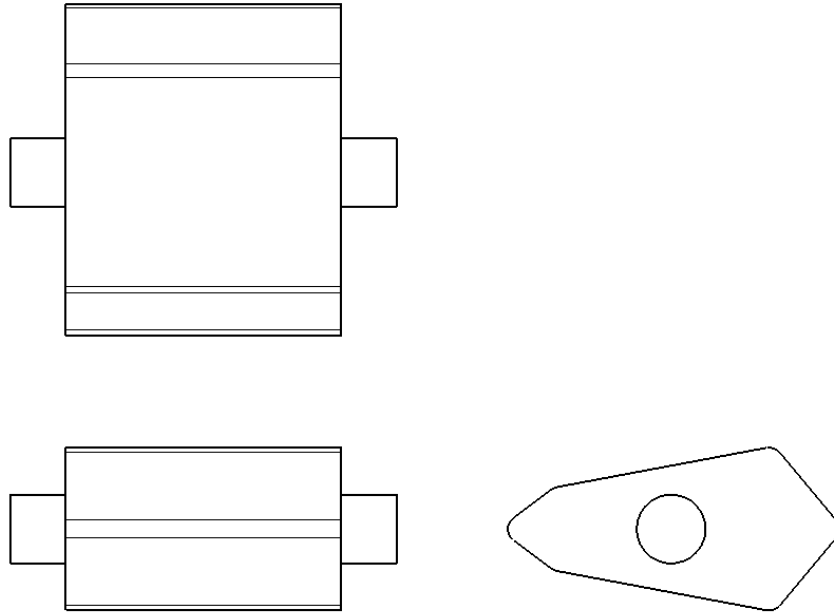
Alzado, perfil y planta de la pieza de acople.
